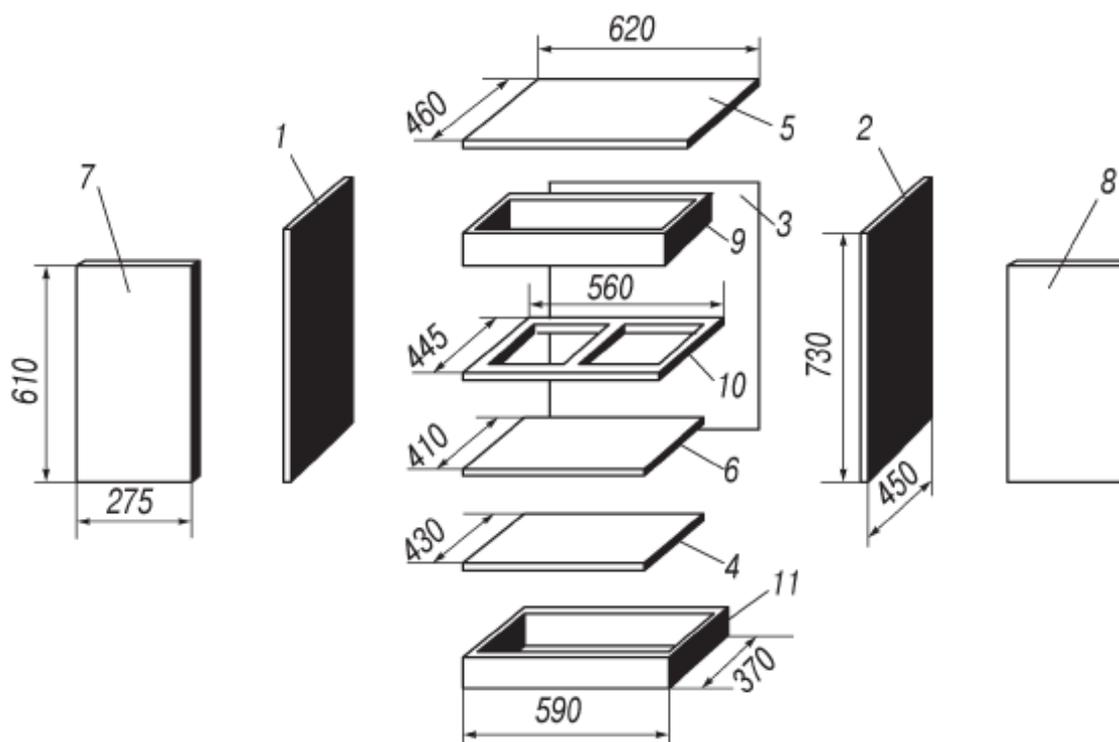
Основные детали разделочного стола-шкафа: 1, 2 – боковые стенки; 3 – задняя стенка; 4 – днище (нижний полк); 5 – крышка; 6 – полка; 7, 8 – дверки; 9 – ящик; 10 – подъящичная рамка; 11 – цоколь
